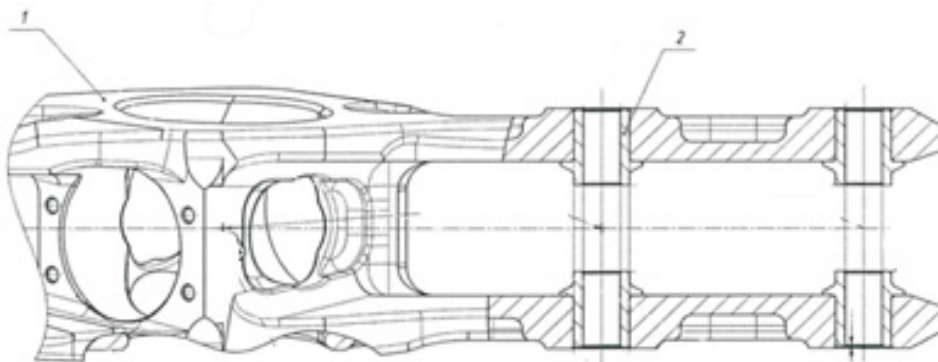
Конструктивная схема корпуса втулки рулевого винта вертолета в зоне крепления лопастей:
